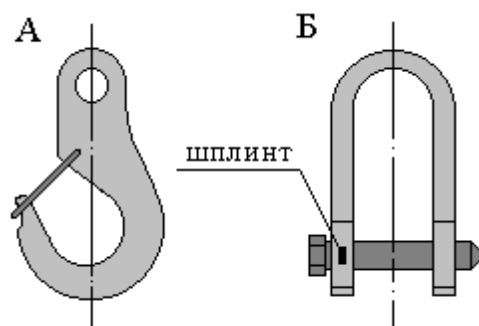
Захваты: А – чалочный крюк, Б – такелажная петля
